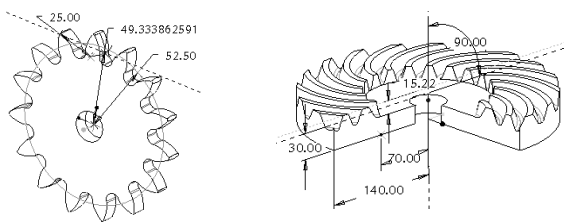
Основні розміри циліндричного (а) та конічного (б) коліс
